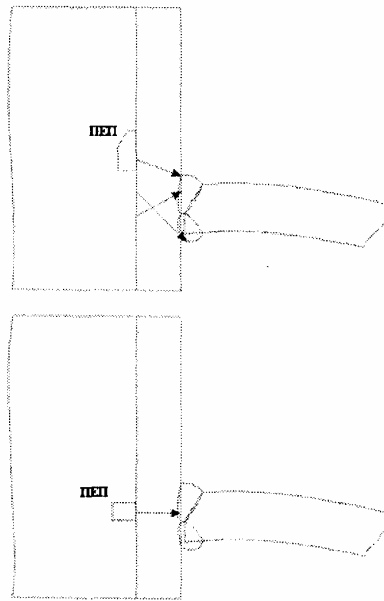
Схемы контроля углового сварного соединения штуцера по внутренней поверхности
